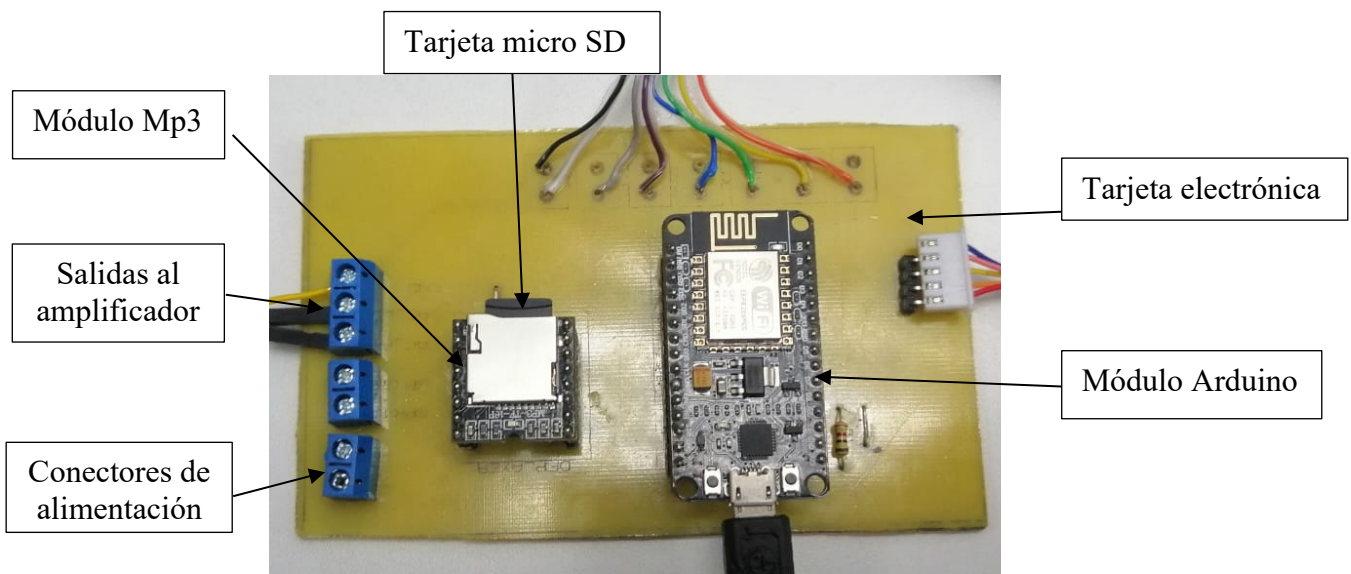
Placa electrónica *Fuente*. placa electrónica con todos los componentes electrónicos soldados, elaborado por el autor.
